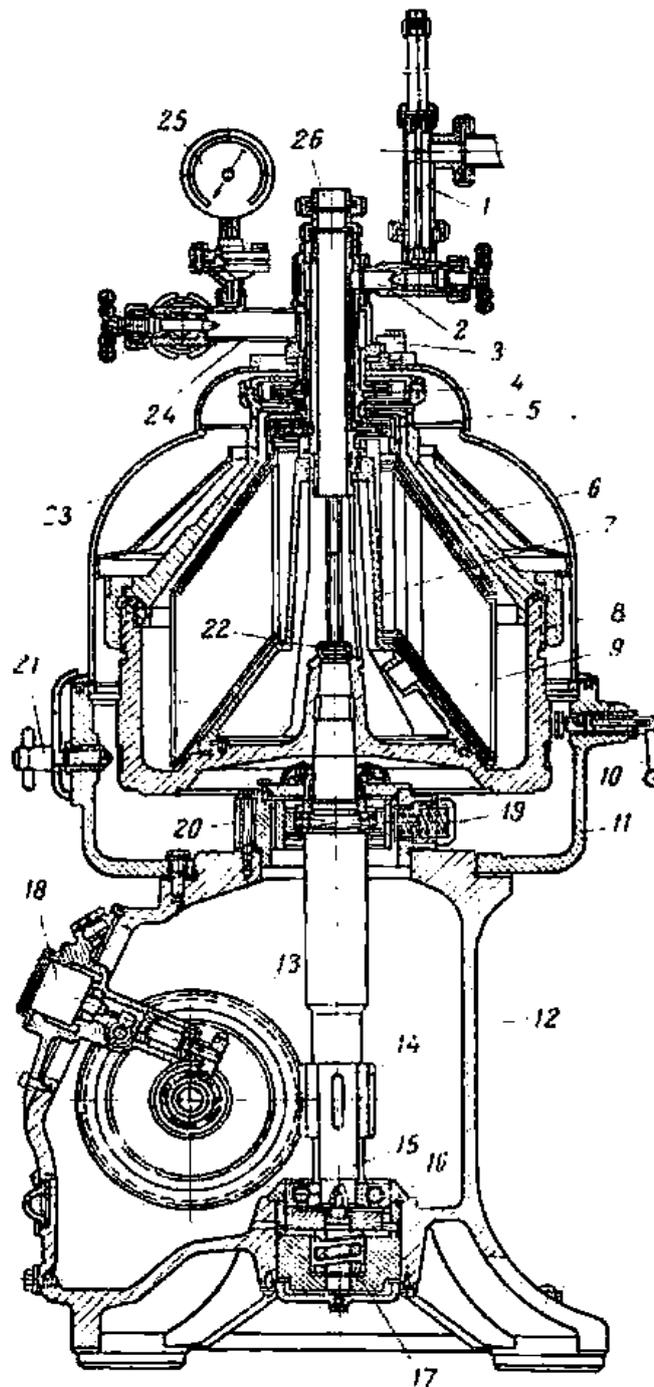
4. Полугерметический сепаратор ОСИ производительностью 10 000 л/ч: 1 — поплавковый ротаметр; 2 — патрубок для ОТВОДА челнок; 3 — зажимы; 4 — напорный диск для обезжиренного молока; 5 — напорный диск для сливок; 6 — крышка барабана; 1 — тарелкодержатель; 8 — основание барабана; 9 — пакет тарелок; 10 — рукоятка тормозной колодки; 11 - чаша станины; 12—основание станины; 13 — винтовое колесо; 14 - шестерня веретена; 15 — вертикальный пал (веретено); 16— упорный сухарь; 17 — упорная пружина; 18— тахометр; 19 — пружины горловой опоры; 20 — корпус горловой опоры; 21 — стопорный винт; 22 — предохранительная гайка; 23 - кожух; 24 - патрубок для отвода обезжиренного молока; 25 — манометр; 26 - центральная трубка.
